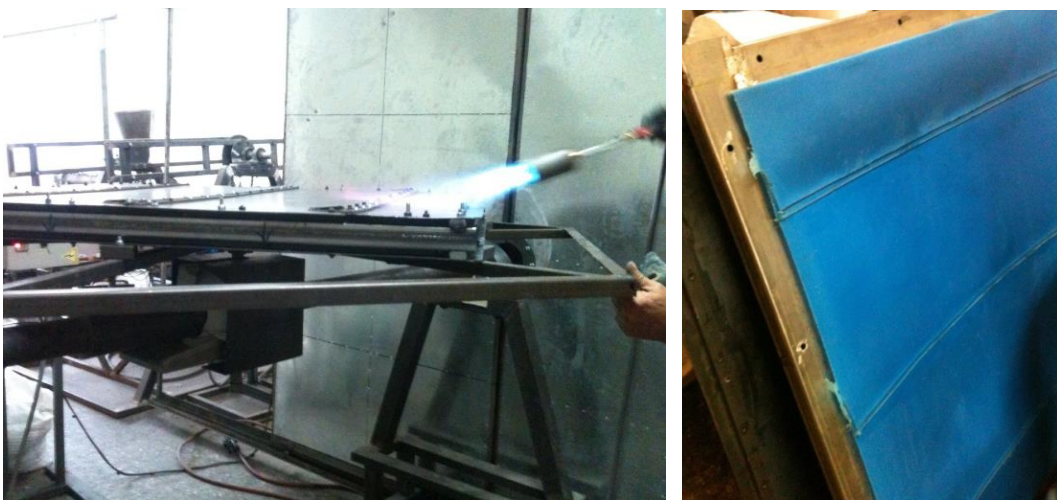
Enfriamiento del molde para el desmolde de la pieza
